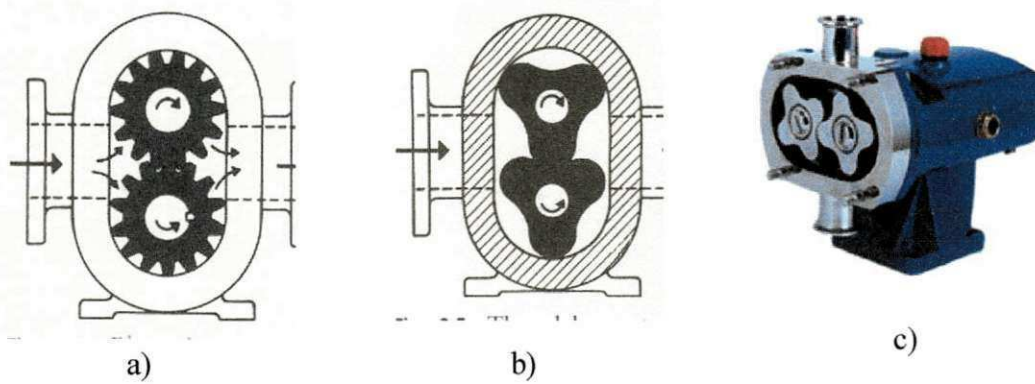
Cortes de bombas rotativas a) Bomba de engrenagem comum. b) Bomba de rotor trilobulado. (Fonte: Hick and Edwards 1971) c) Bomba rotativa quadrilobular moderna.
